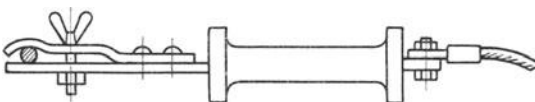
Schweißkolben für Warmschweißungen.
